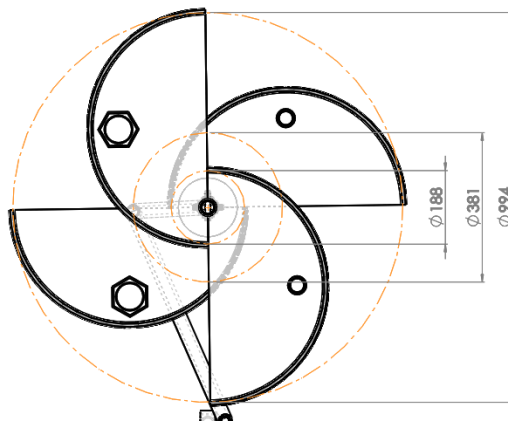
Vista superior del rotor con sus dimensiones (Dimensiones en milímetros).
